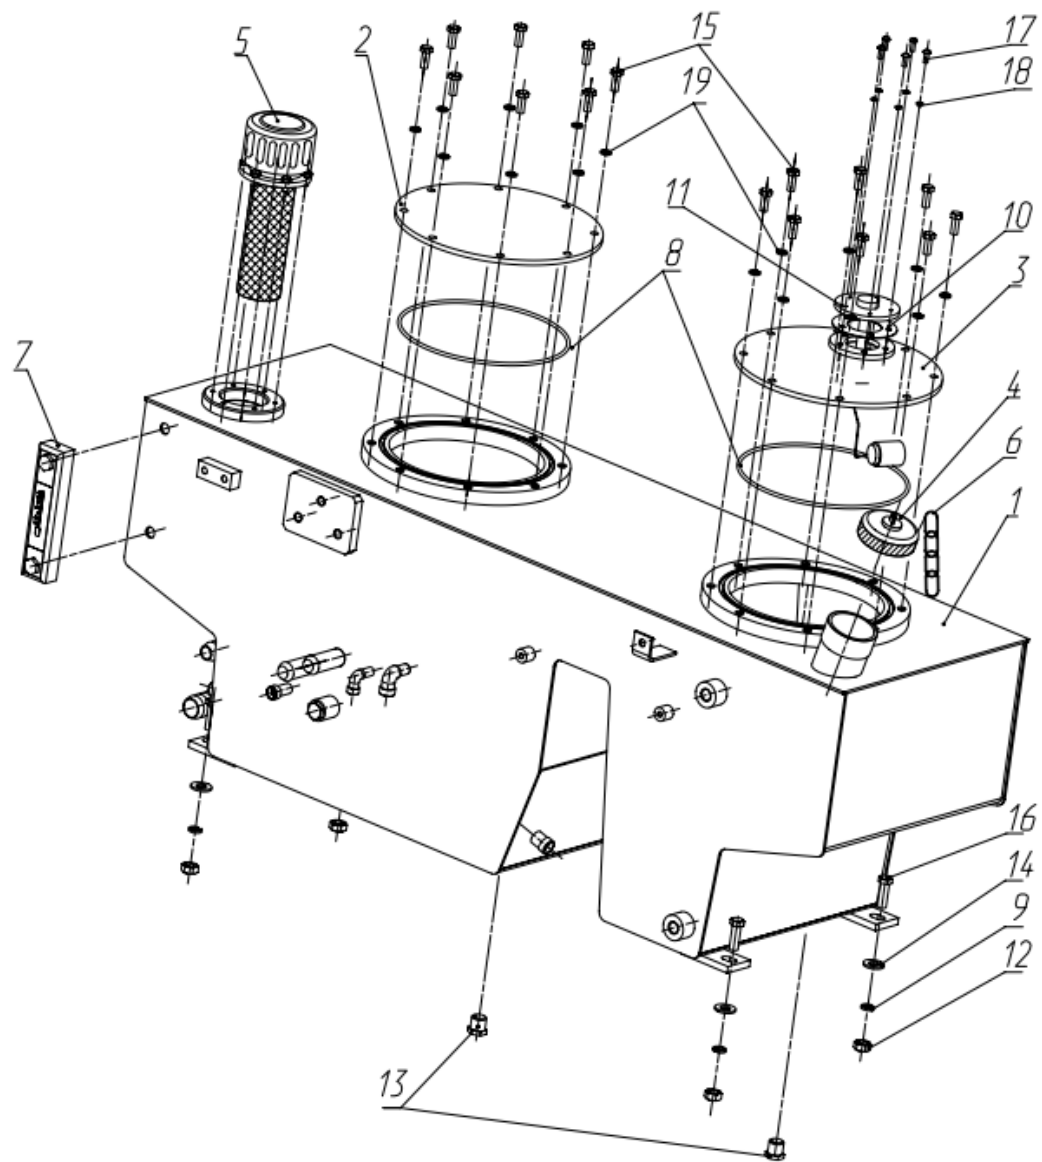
/ Fig.22 6222.27.00.000-01 Установка баков / Instalng the tanks
